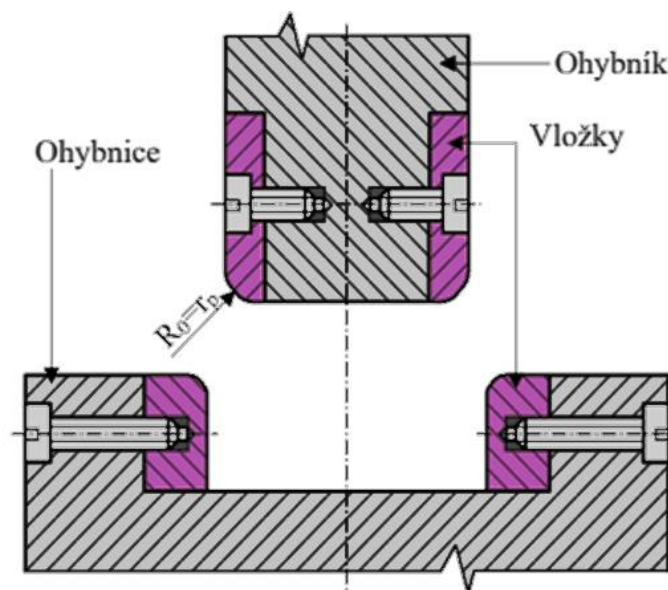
Tolerance a funkční rozměry nástrojů [50].
